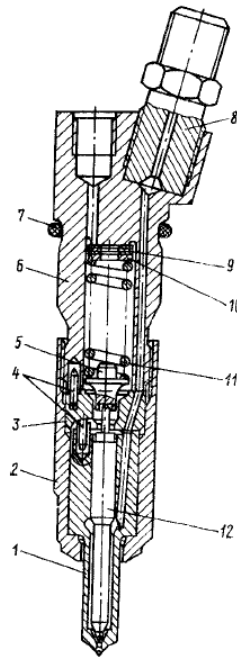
Форсунка: 1 - корпус розпилювача; 2-гайка розпилювача; 3 - проставивка розпилювача; 4 - штифти установчі; 5 - штанга форсунки; 6 - корпус форсунки; 7 - кільце ущільнювача; 8 - штуцер; 9, 10-шайби регулювальні; 11 пружина форсунки; 12-голка розпилювача
